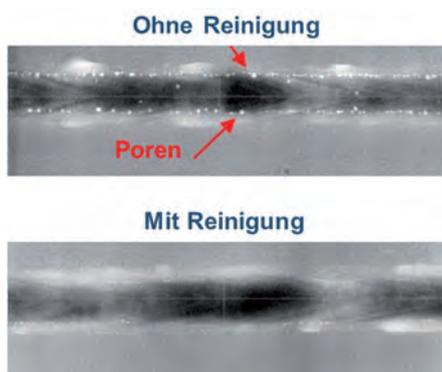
Querschliff lasergeschweißter Aluminiumbleche mit und ohne Laserreinigung (AlMn1Cu + AlMg3)
